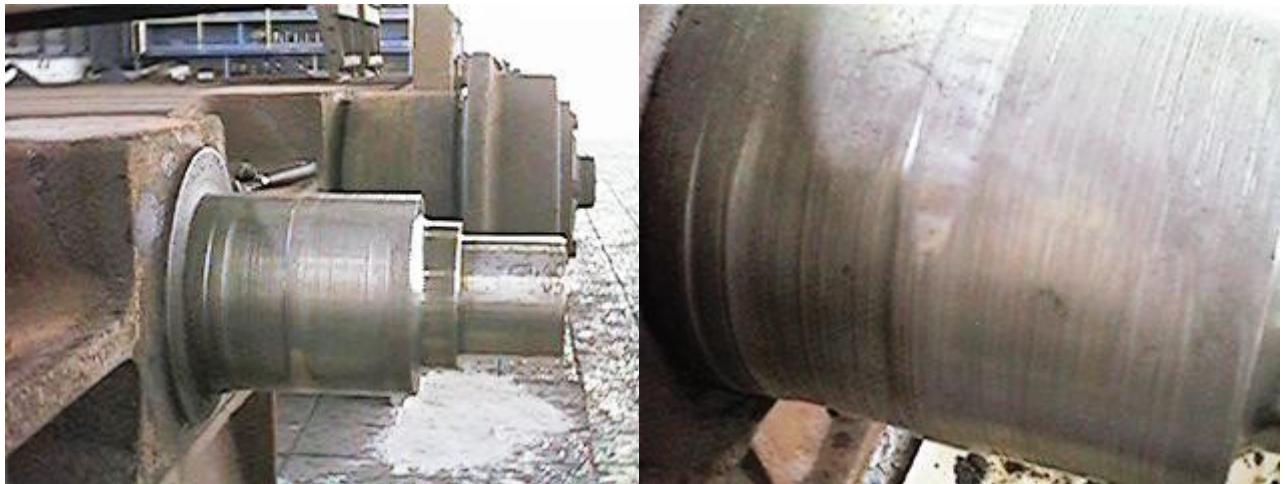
Detalhes do eixo das caixas de Sinter, após a retirada do rolete, apresentando o desgaste.
